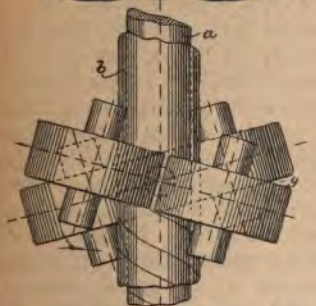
Disposizione dei rulli cilindrici vista dall'alto.
